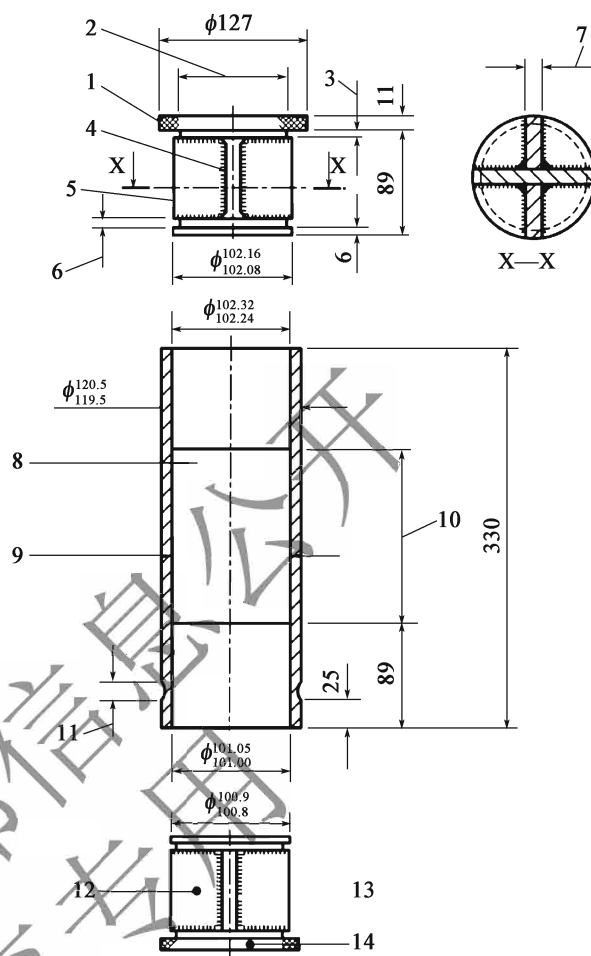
击实筒和端部螺塞示意图 (尺寸单位: mm)
